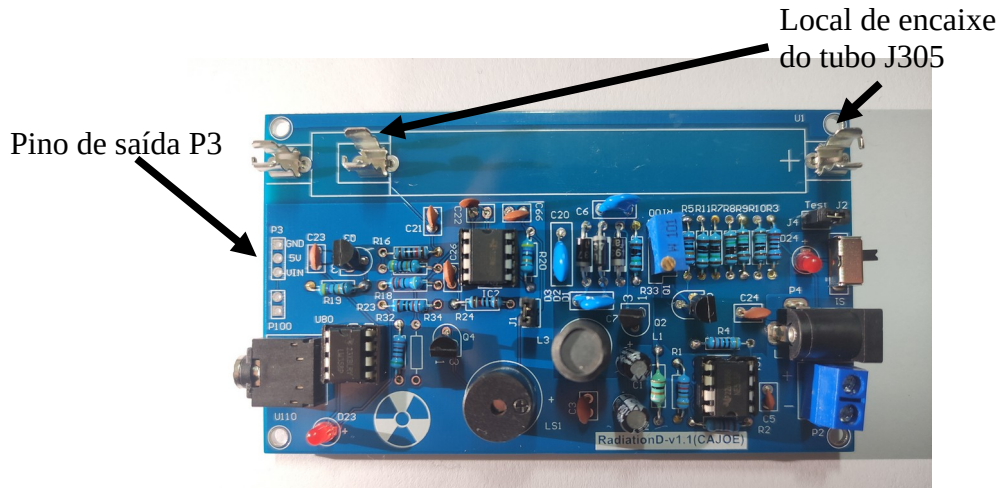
Placa do circuito com todos os componentes soldados, onde é possível observar o encaixe para o tubo Geiger-Müller. Fonte: O Autor (2024).
